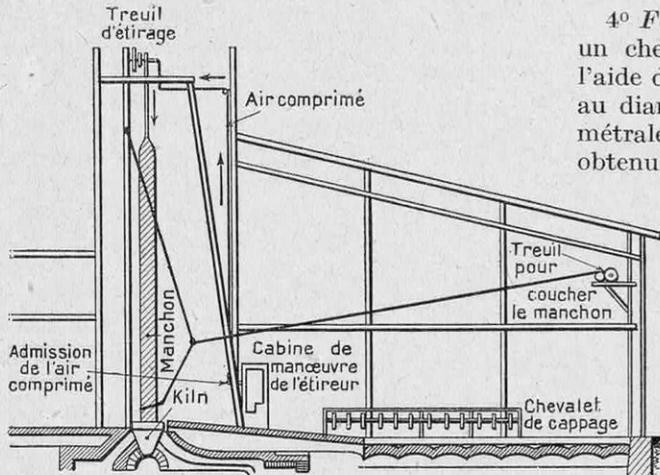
COUPE LONGITUDINALE D'UN ATELIER DE L'AMERICAN WINDOW GLASS, MONTRANT LE MANCHON DE VERRE TERMINÉ EN POSITION VERTICALE
